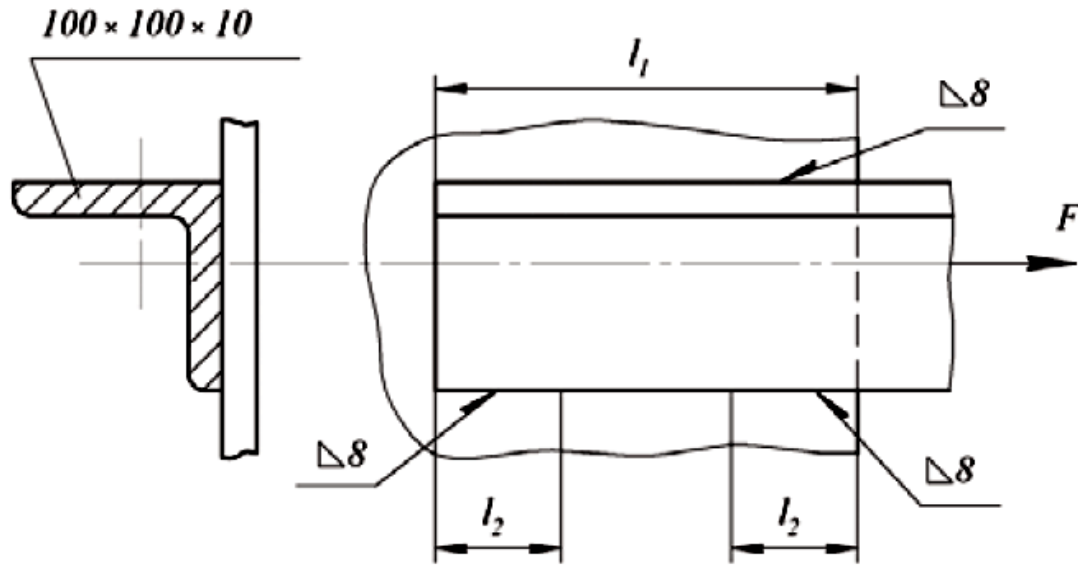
Сварное соединение уголка с пластиной угловыми швами
